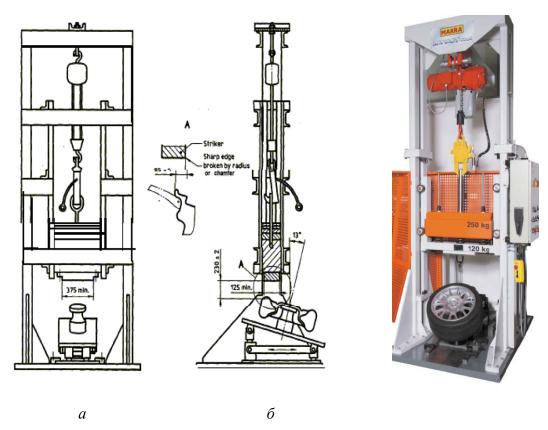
Принципиальные схемы (а и б) и общий вид стенда для испытаний колес на удар под углом 13°
